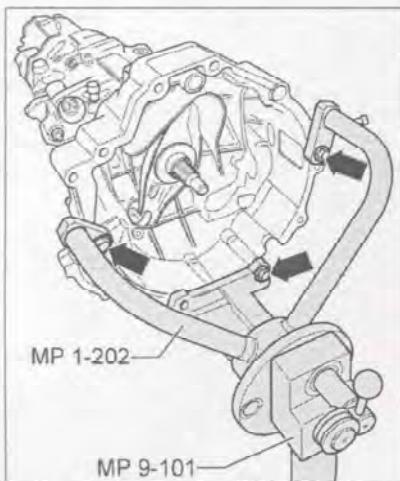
Закрепите коробку передач на сборочном стенде (стрелки).
